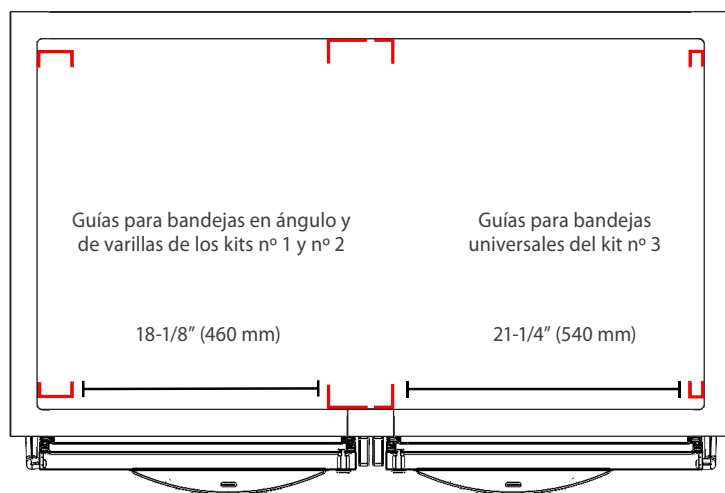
Mida la distancia entre las columnas. Vista de arriba a abajo.
